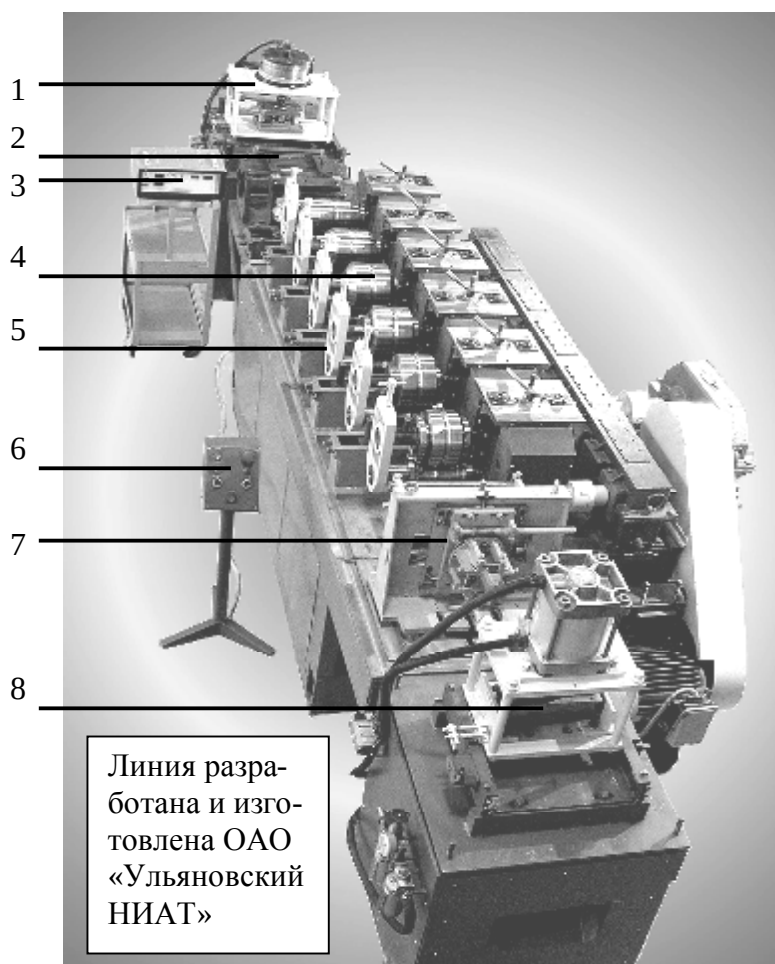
Автоматическая линия профилирования на базе станка ГПС-300М6 (разматывающая рулонница и приемный стол условно не показаны): 1 – перфоратор; 2 – направляющее устройство; 3 – отсчитывающее устройство; 4 – клеть станка; 5 – серьга зажимающая; 6 – пульт управления; 7 – правильное устройство; 8 – летучий штамп отрезной
